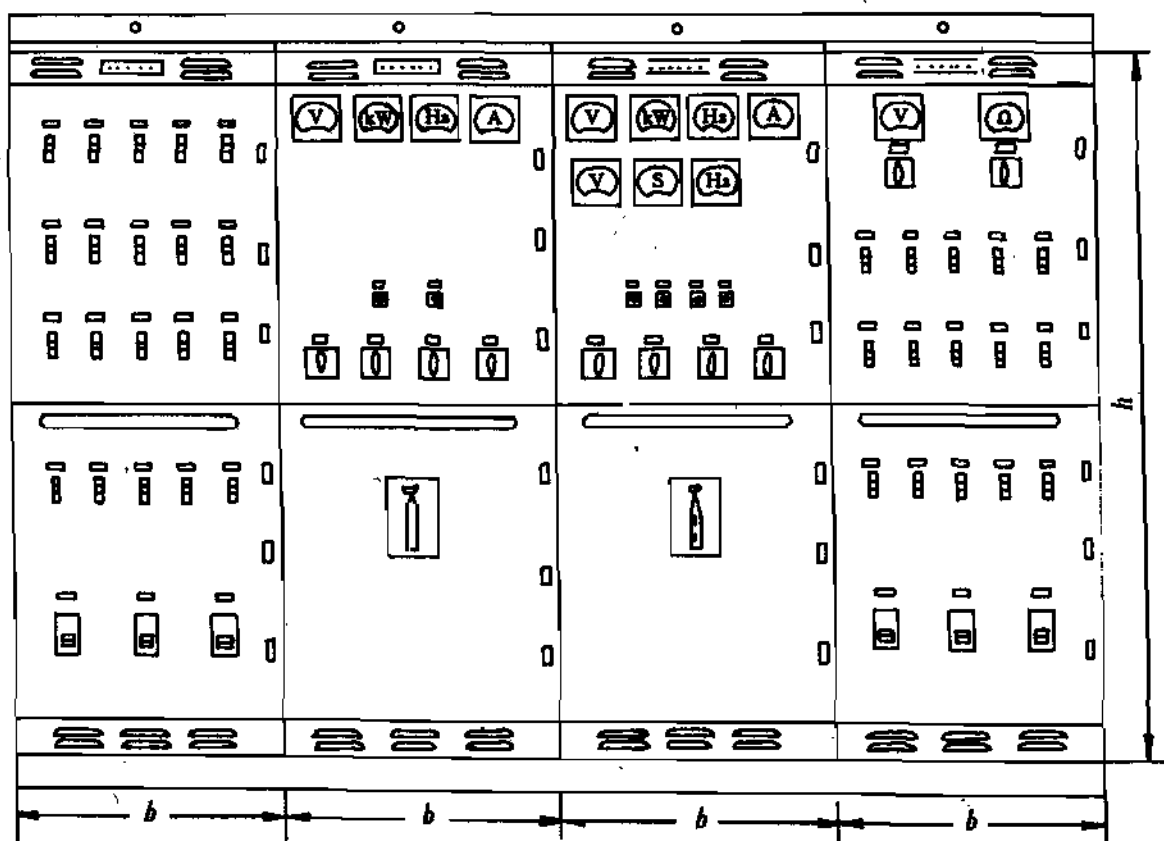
封闭式主配电板主要电器元件布置示意图
